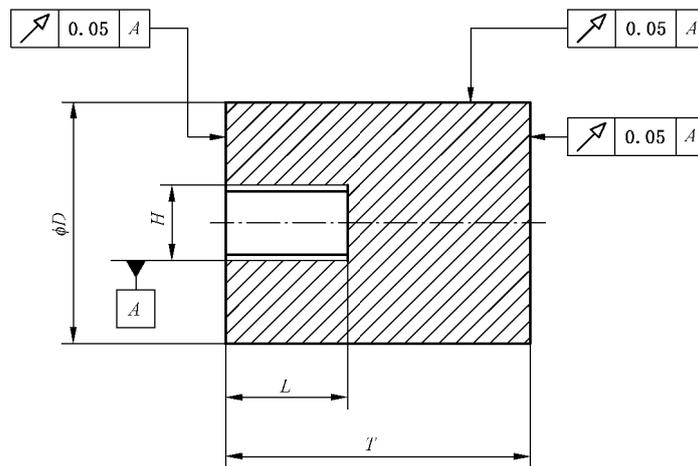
1 型平形试验轮的尺寸和公差
